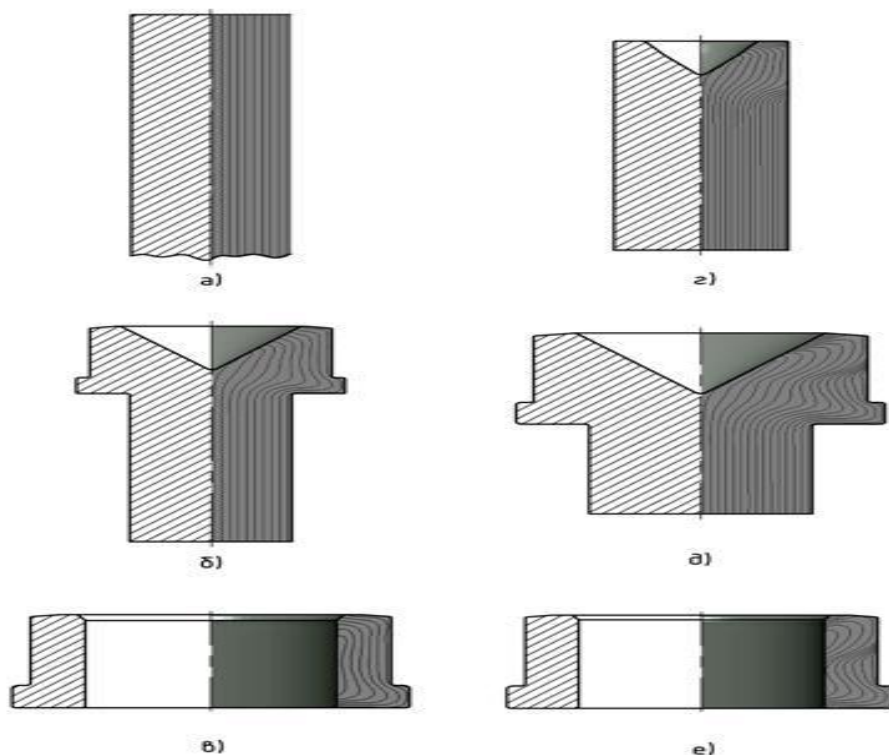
Моделювання штампування поковки кільця на ГКР в пуансоні: а - вихідний пруток; б - формування 1-ої поковки; в - перша кування; г - пруток після просечки; д - формування 2-ий поковки; е - друга кування
